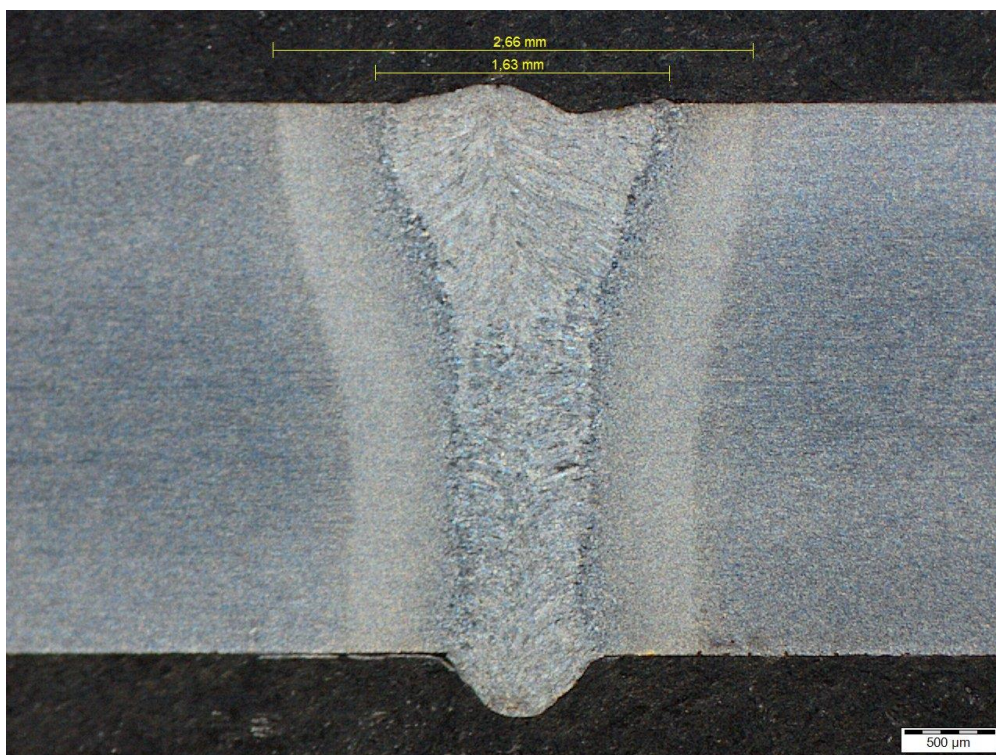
Makrostruktura svaru (laser s přehřevem TIG – vzdálenost elektrody 1 mm)
